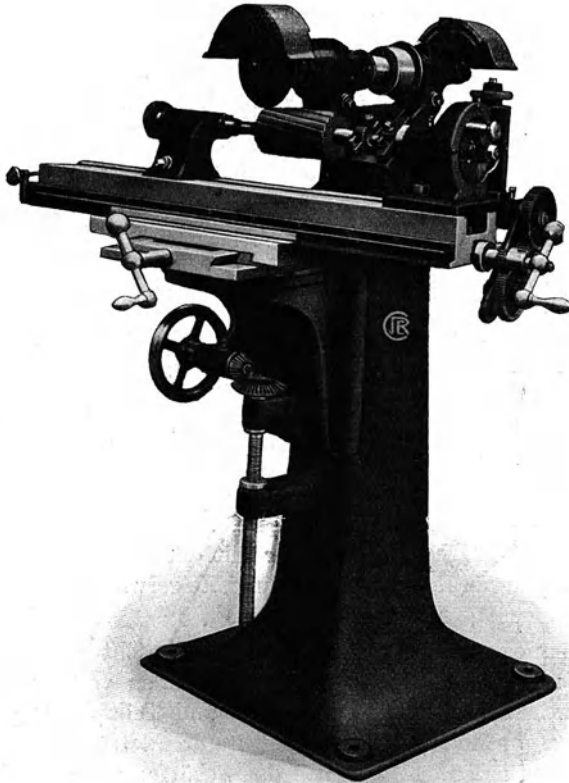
Die Reineckersche Fräuserschärfmaschine mit Teilapparat.
